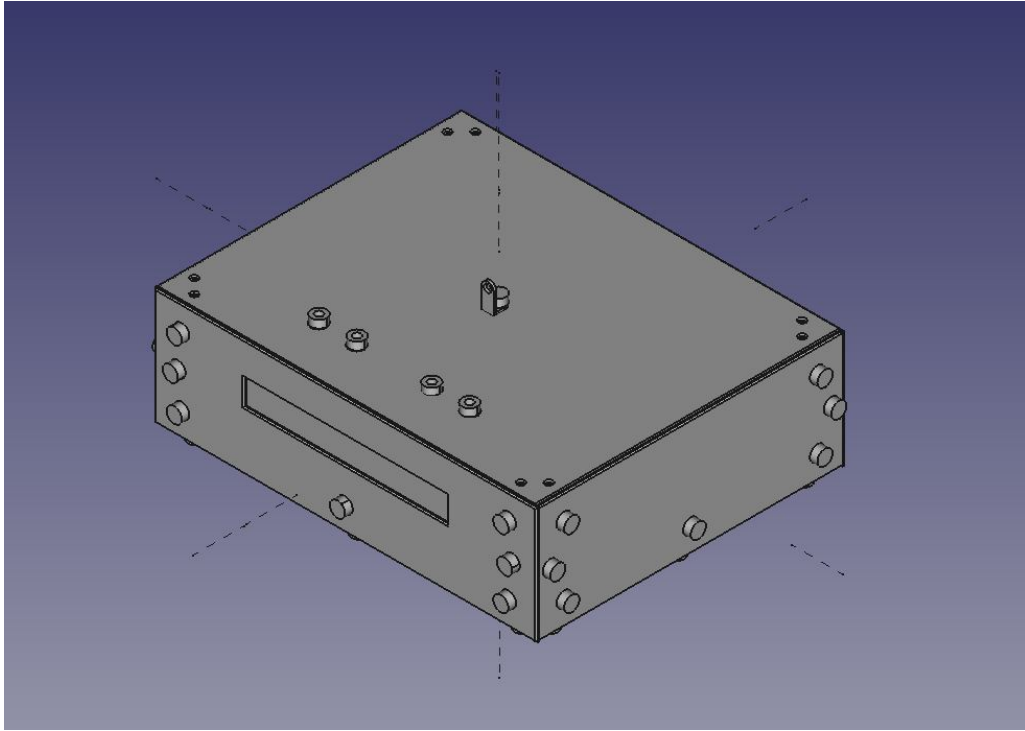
Vista isométrica de la carcasa ensamblada, creado con FreeCAD.
